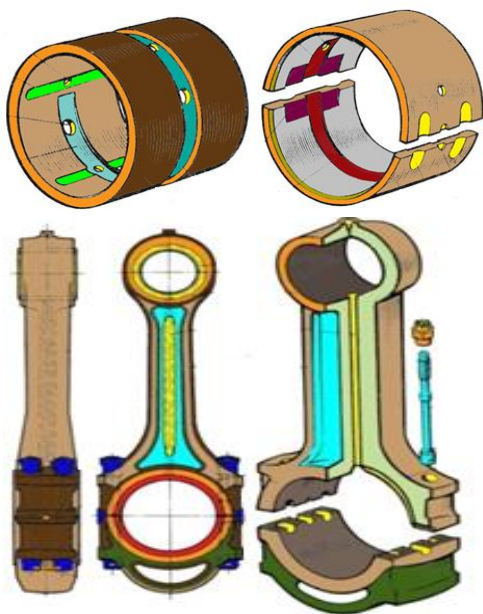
Шатуны и шатунные подшипники дизеля 310DR
